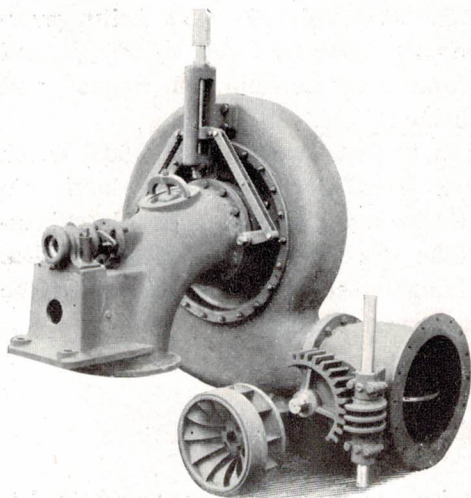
Spiralturbine mit herausgenommenem Laufrad.
